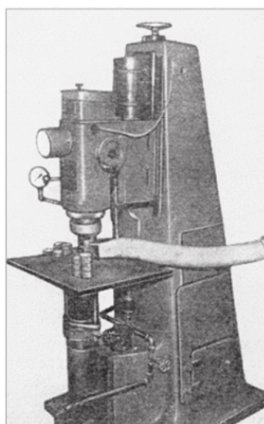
Пескоструйный прибор для определения твердости абразивных инструментов (общий вид)
